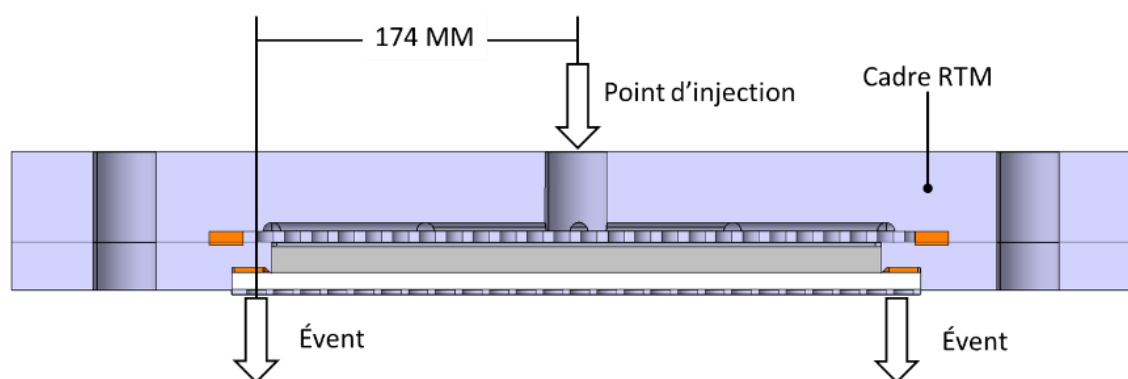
Vue de coupe de l'assemblage du moule RTM adapté aux CMC
